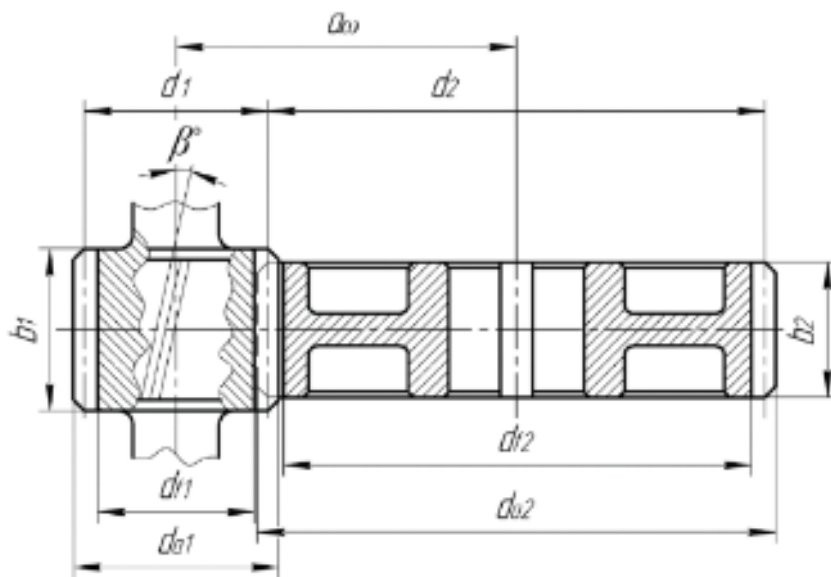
Геометрические параметры цилиндрической зубчатой передачи
